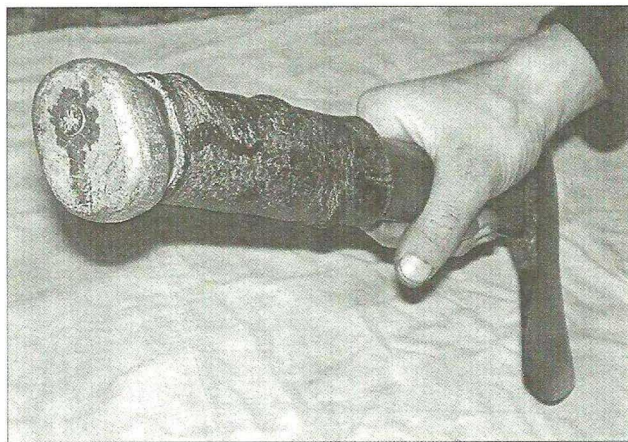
Сварка заглушки и развальцованного переднего среза (торца) топорика с обухом топора
